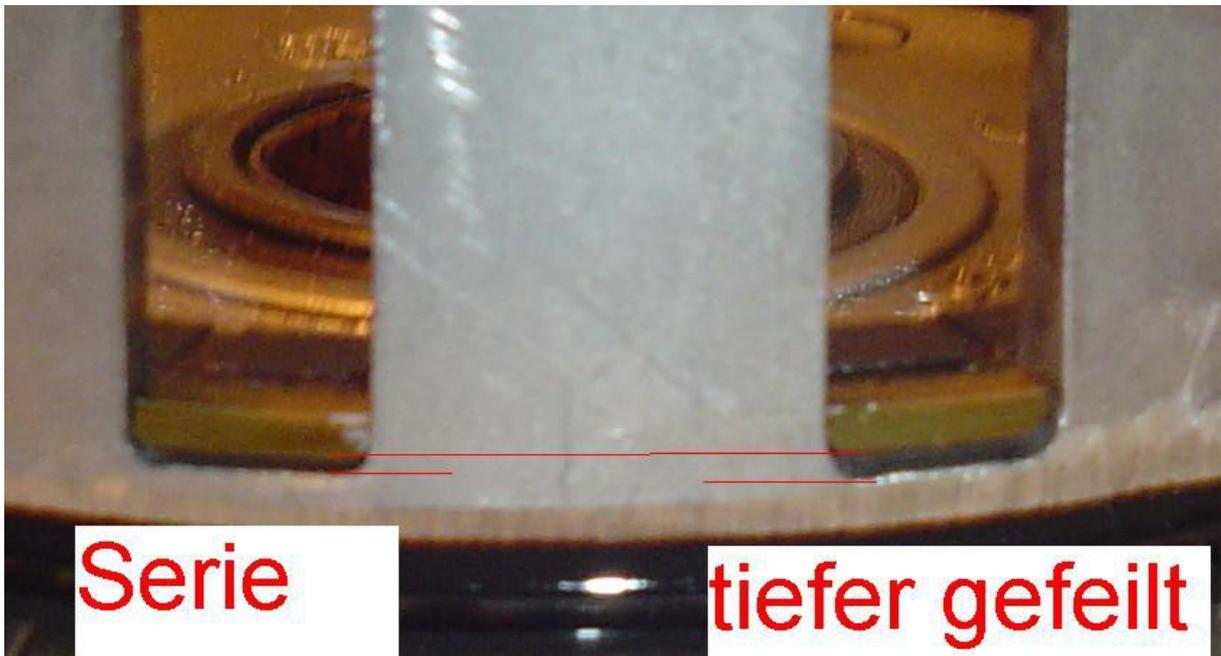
Oben: Bearbeitung der Nuten im Kupplungskorb
